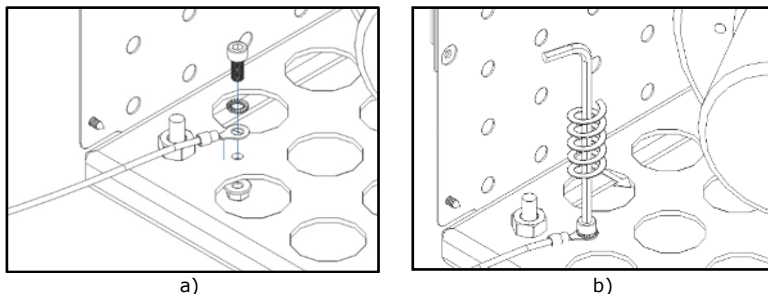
Conexión del cable de puesta a tierra del ventilador
